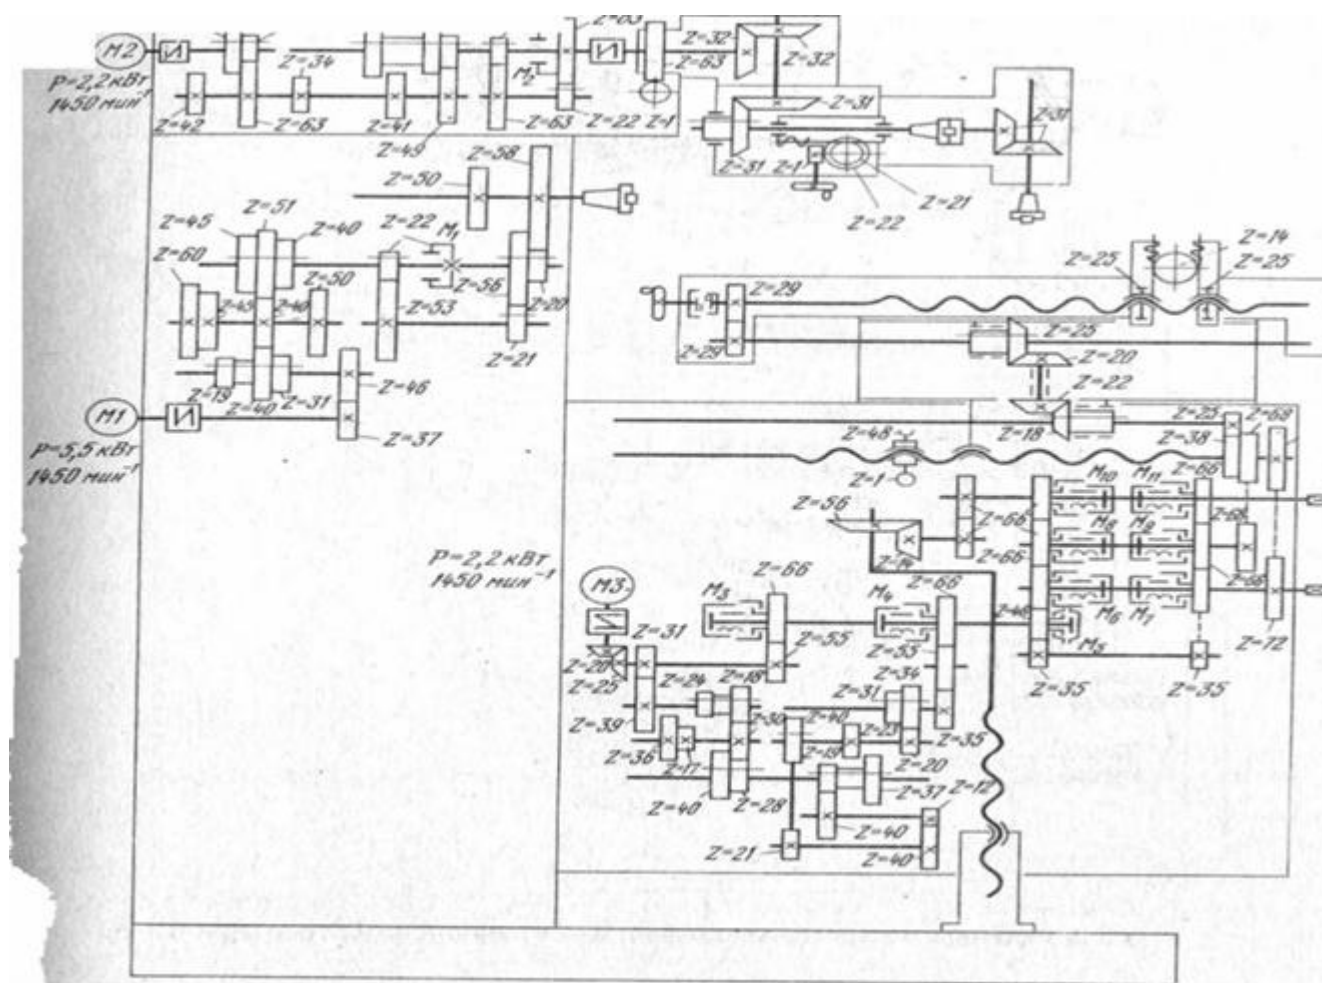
Кинематическая схема станка мод. 6Д82Ш.
